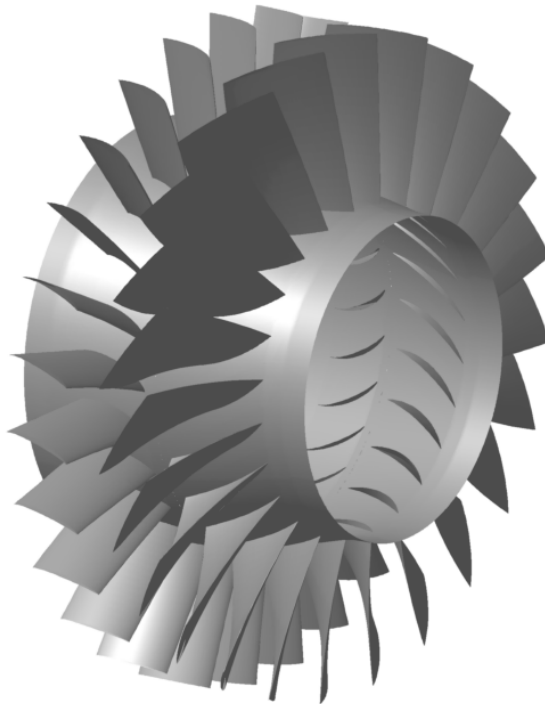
3D-Ansicht des Axialverdichterentwurfs
